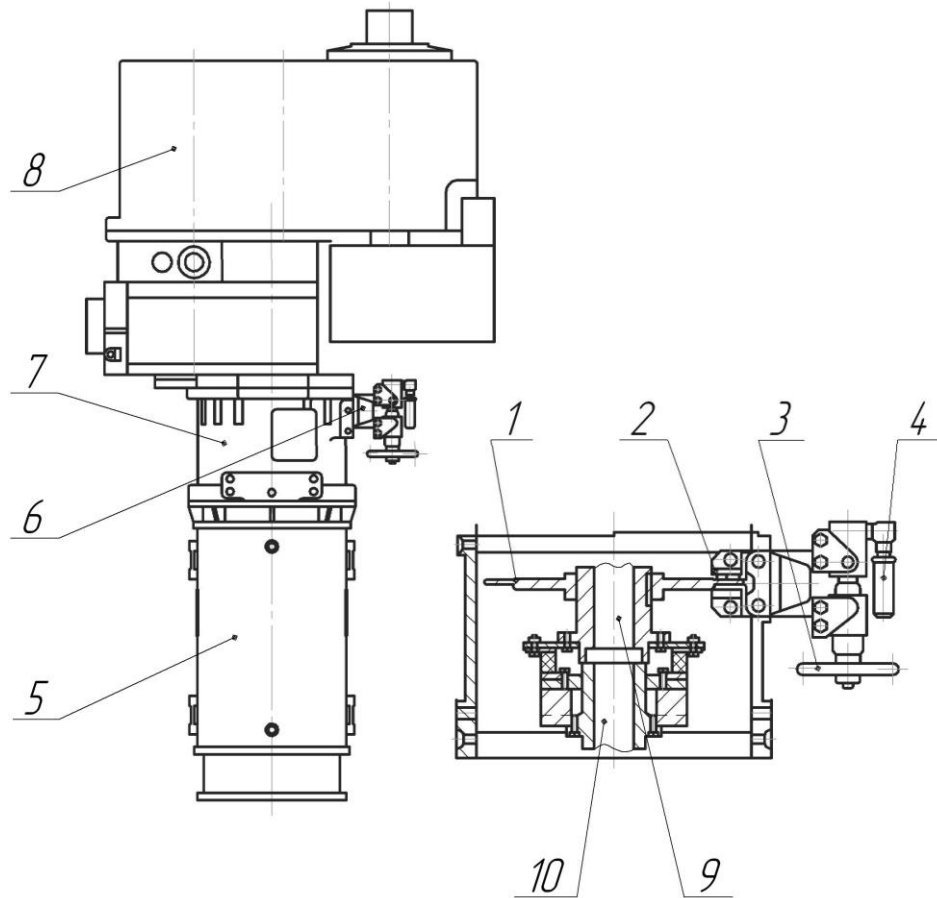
Гидрокинематическая схема низкодинамического натяжного устройства
